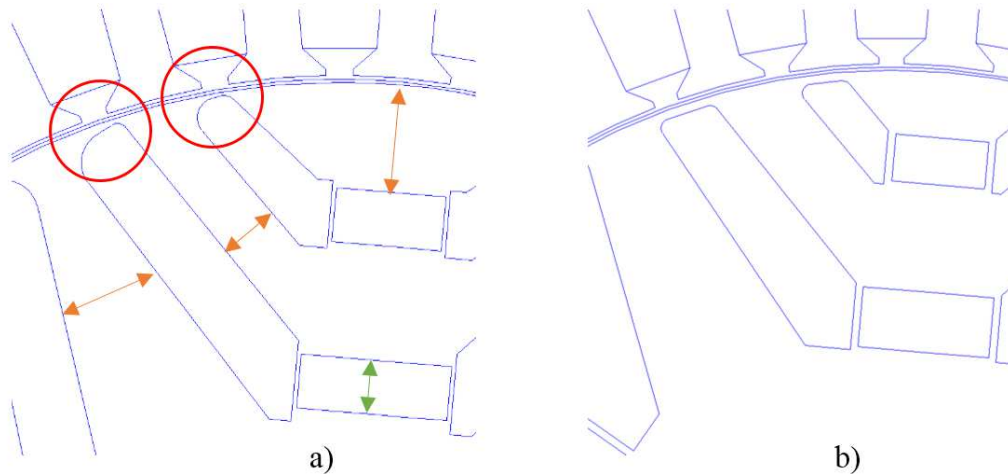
a) Disseny inicial del rotor. b) disseny final del rotor del motor PMASynRM
